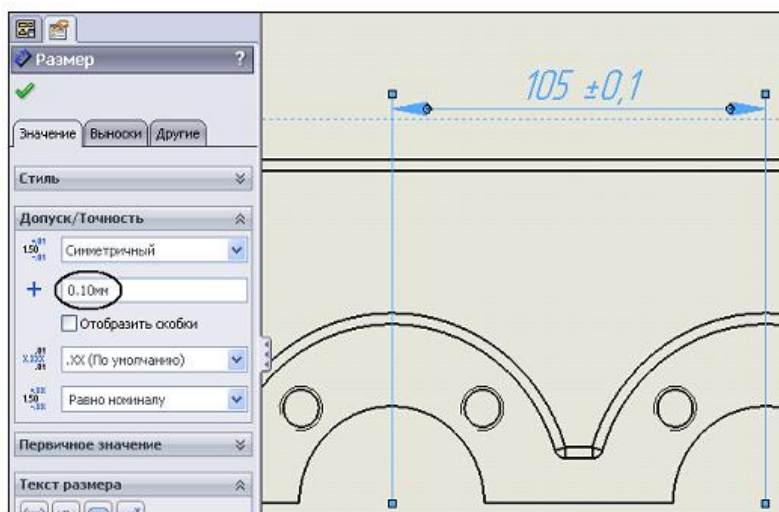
Нанесення допуску на креслення
